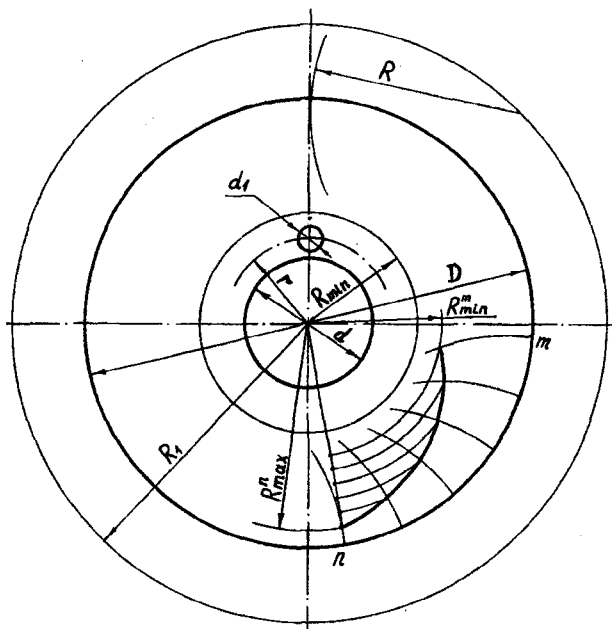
Чертеж заготовки кулачков суппортов и схем построения профиля кулачка
